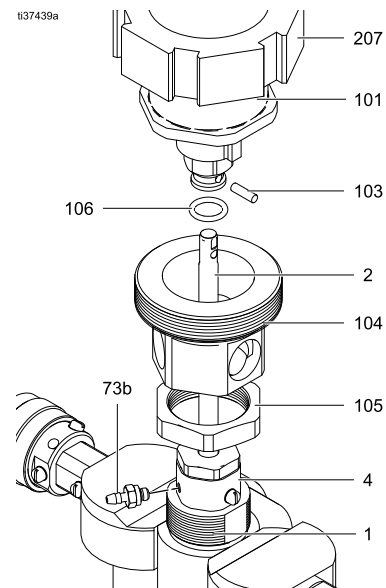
Wiederanschluss der Unterpumpe mit dem Antrieb
